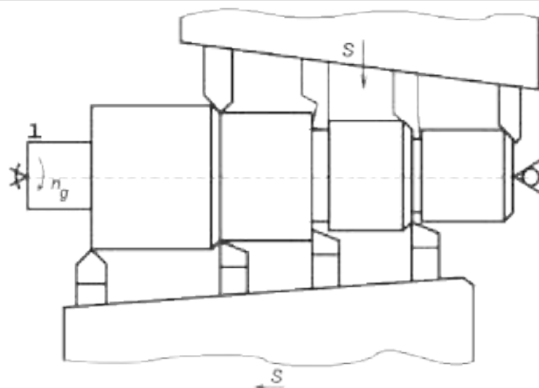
Схема обробки вала на багаторізцевому напівавтоматі
